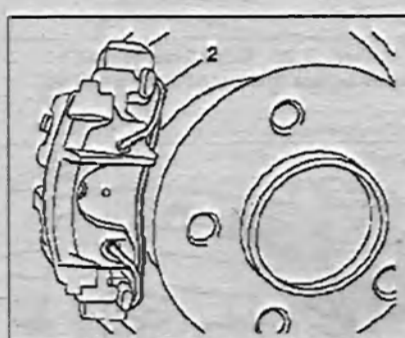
Отсоедините и снимите пружинный фиксатор 2.
